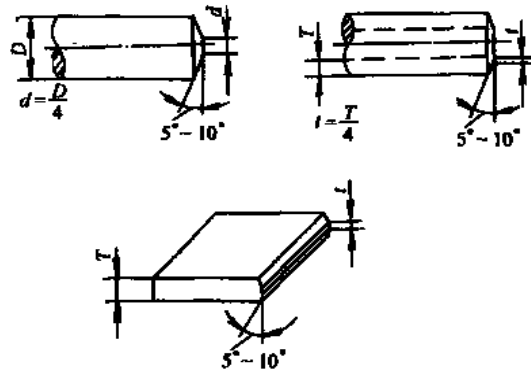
闪光对焊焊件端部的倒角尺寸
